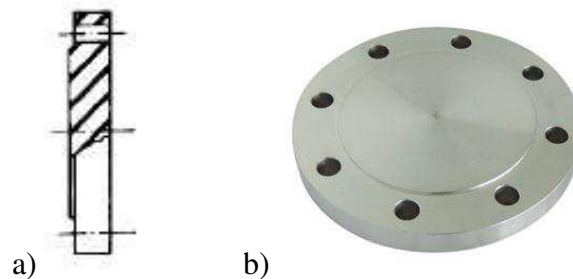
a) Desenho Representativo de um Flange Cego (SENAI, 1997). b) Flange Cego (AHAD Tubeline co., 2012)
